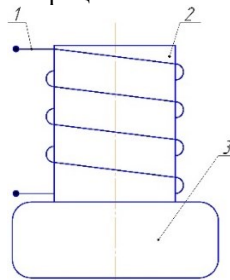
Схема індукційного нагрівання: 1- індуктор; 2- частина заготовки що підлягає деформуванню; 3- матриця
